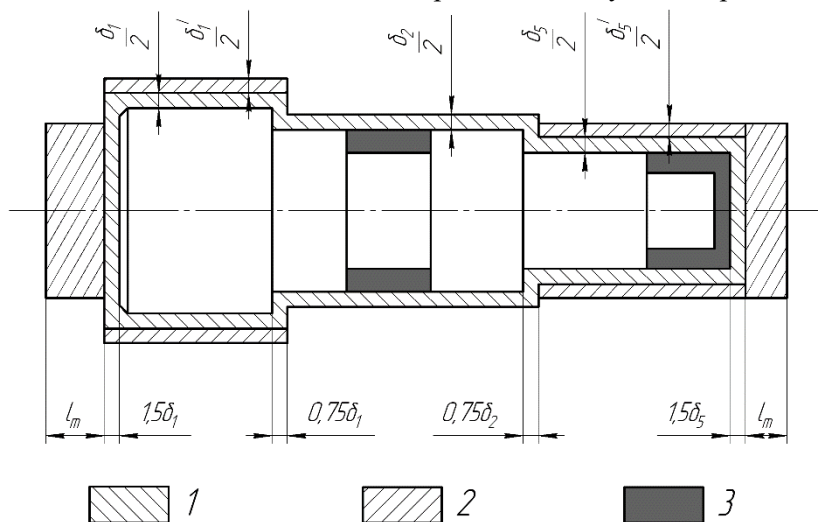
Эскиз детали с основными (1), дополнительными (2) припусками и напусками (3)
